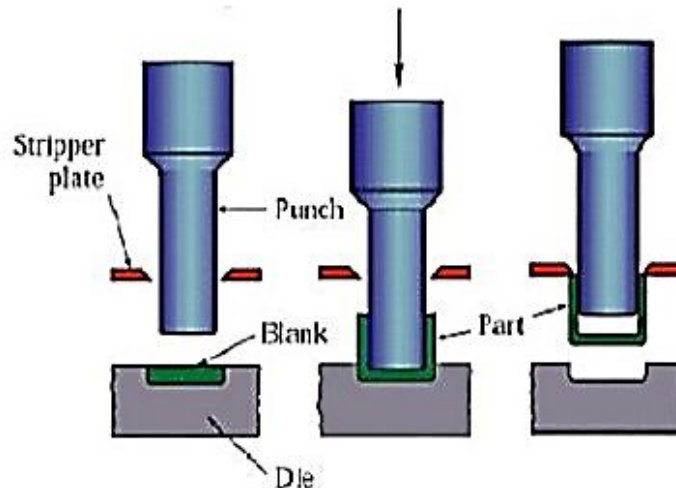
Esquema del proceso de extrusión por impacto. Las partes extruidas se desprenden usando una placa desmoldeadora, ya que tienden pegarse al punzón.
